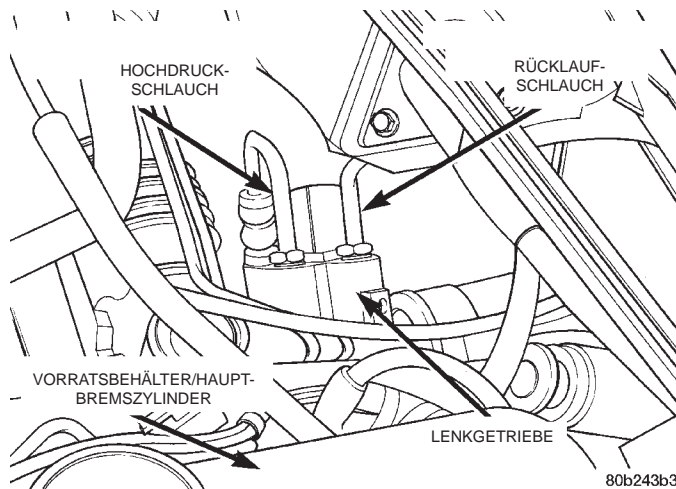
Anschlüsse/Ölschläuche an Lenkgetriebe
